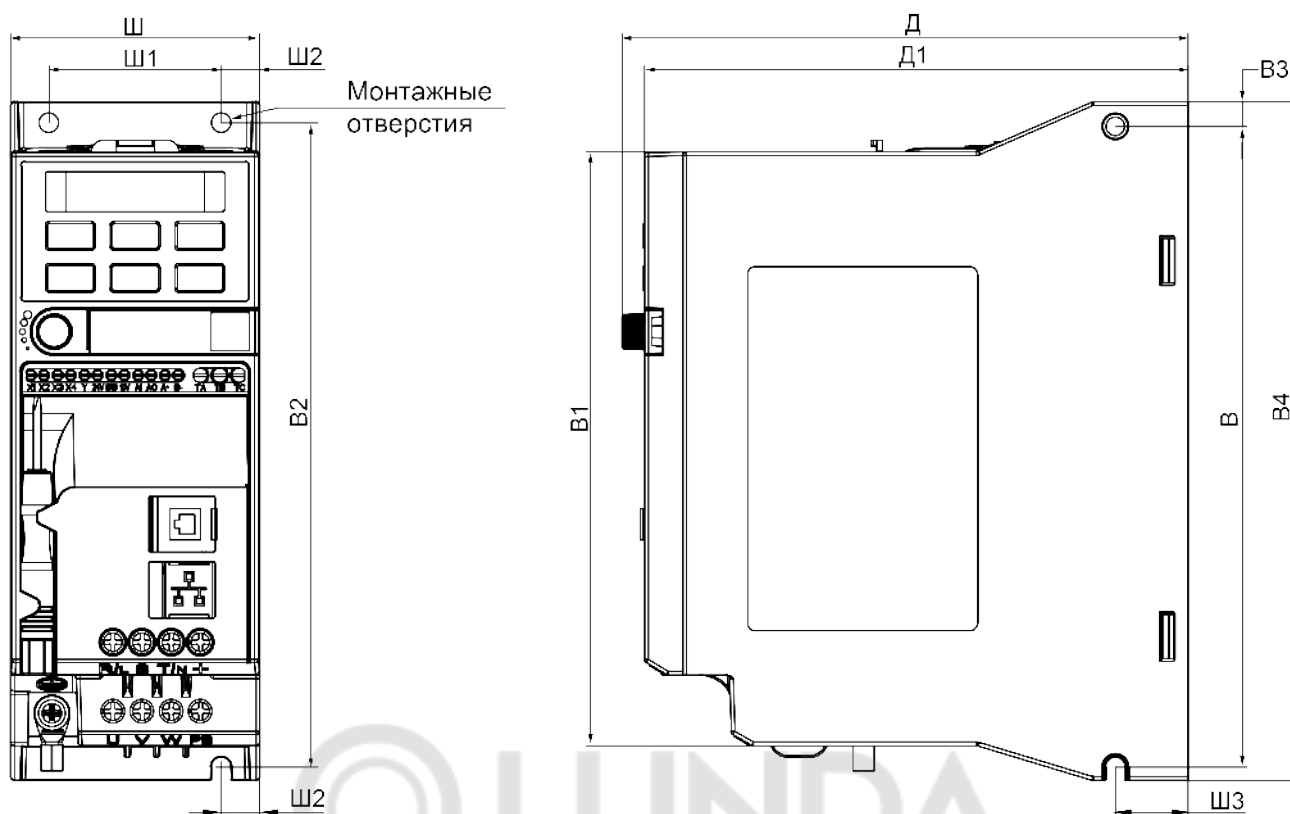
Габаритные и присоединительные размеры прибора типоразмеры 1 и 2
